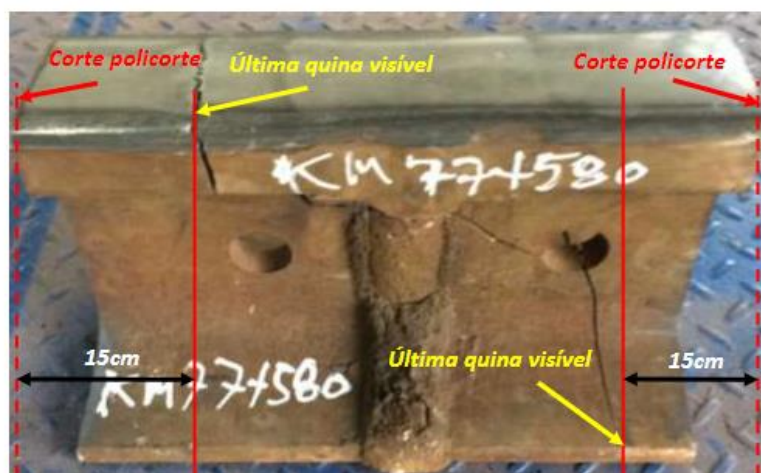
Fratura longitudinal em solda aluminotérmica demarcando regiões a serem cortadas
